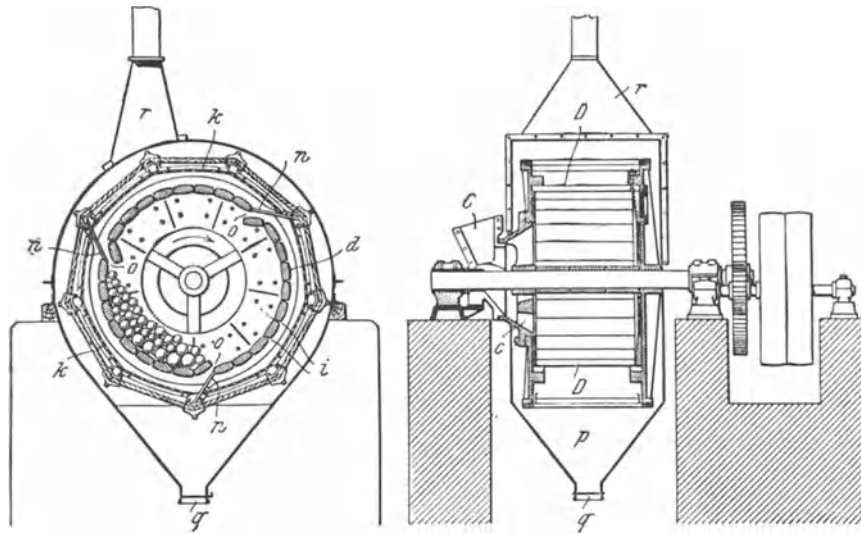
Kugelmühle mit wellenförmiger Fläche.
